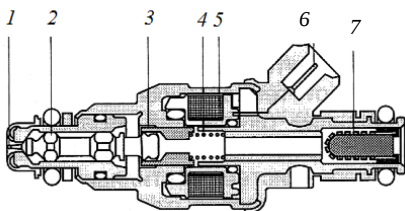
Форсунка системы впрыска L-Jetronic: 1 – штифт; 2 – игла; 3 – якорь; 4 – пружина; 5 – обмотка электромагнита; 6 – электрический контакт; 7 – топливный фильтр
